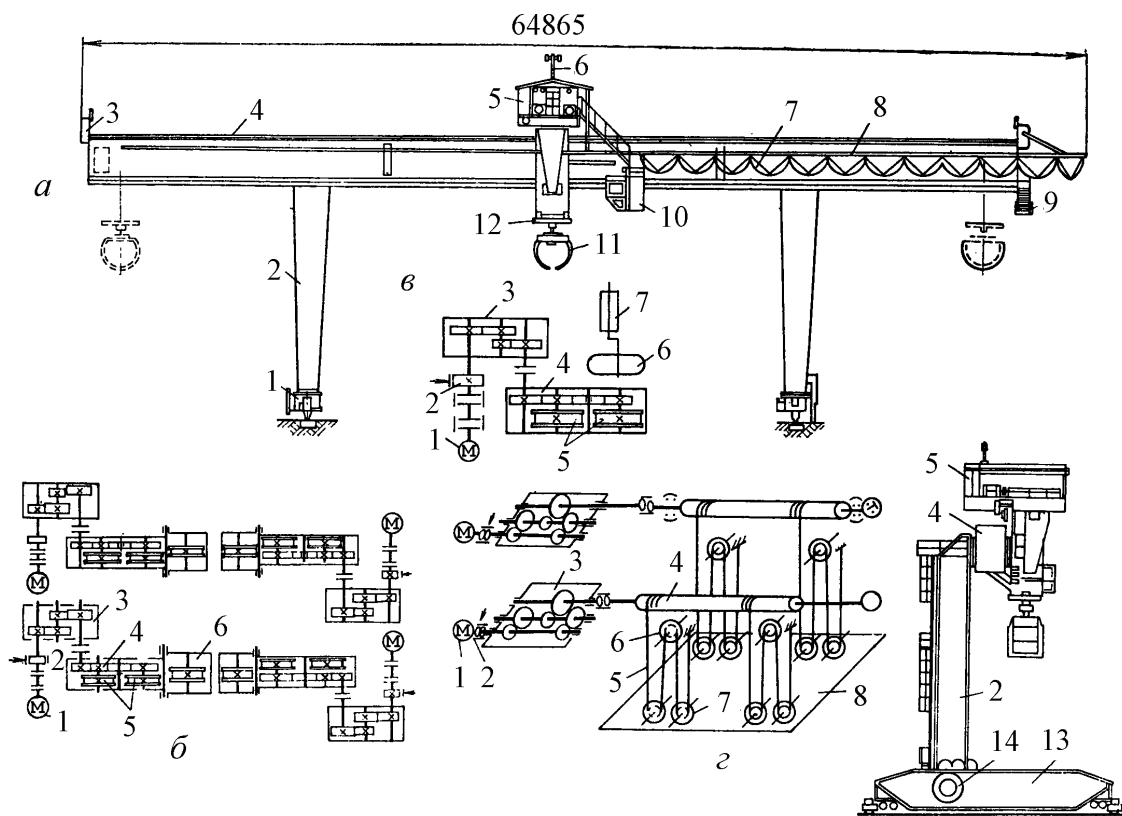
Консольно-козловой кран ККЛ-32: *а* – общий вид; *б* – кинематическая схема передвижения крана; *в* – кинематическая схема грузовой тележки крана;
